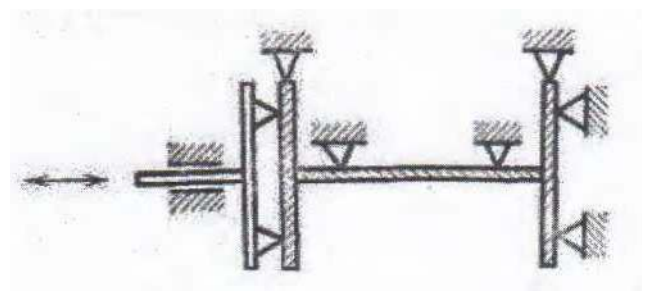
Схема кондуктора для зборки двотаврових балок
